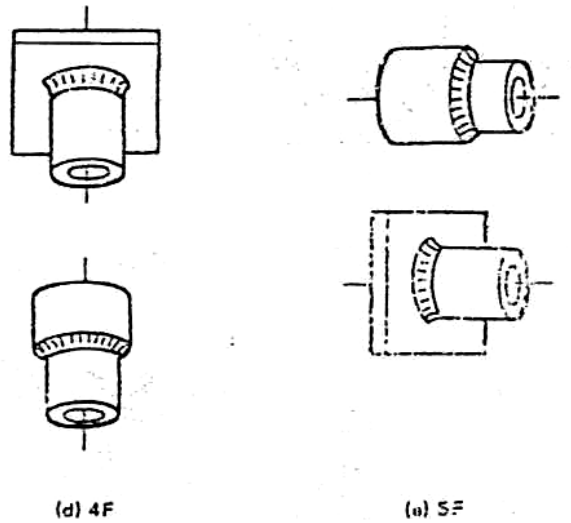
Posiciones de Soldadura en tubo con soldadura de filete
